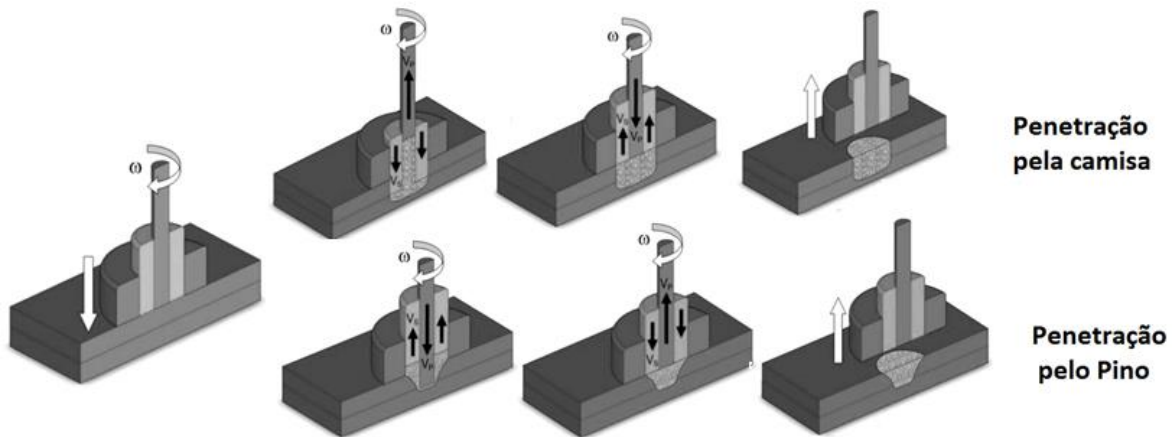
Variações da soldagem FSpW (Penetração pelo Pino e Penetração pela Camisa) e suas etapas (MAZZAFERRO 2009).
